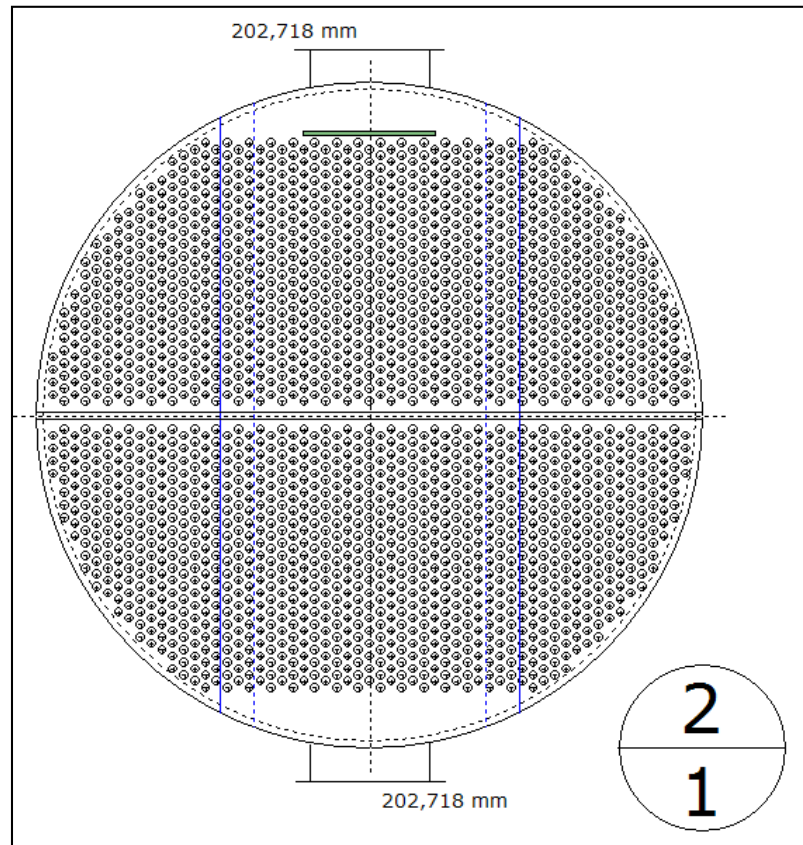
Huella de tubos Recalentador. Fuente: HTRI Output drawing.
